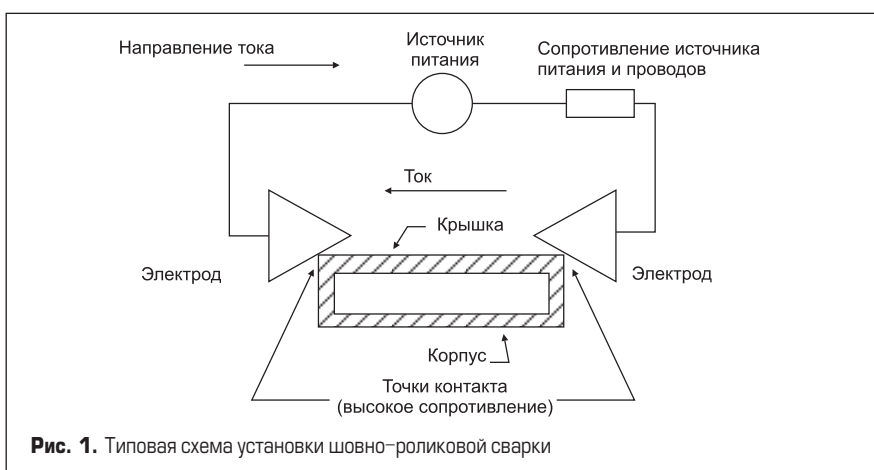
Типовая схема установки шовно-роликовой сварки
